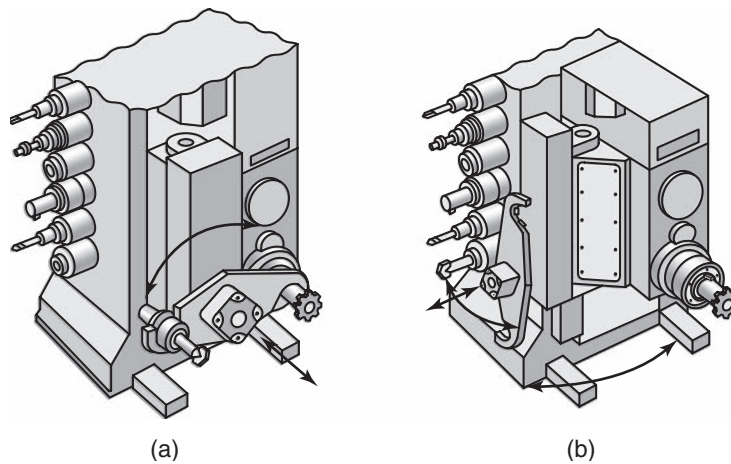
Cambiador oscilante de herramientas en un centro de maquinado de husillo horizontal. (a) El brazo de intercambio de herramientas está colocando un portaherramientas con una herramienta de corte en el husillo de la máquina. Nótese el movimiento axial y rotativo del brazo. (b) El brazo está regresando a su posición de inicio. Obsérvese su rotación a lo largo de un eje vertical después de colocar la herramienta y los dos grados de libertad en su posición inicial.
